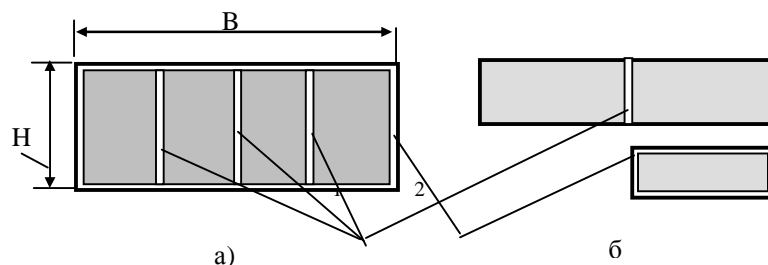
Схемы получения чистовых заготовок (делянок) из черновых заготовок для толстых (а) и тонких (б) досок: 1 - пропилы; 2 - припуски на фрезерование.
